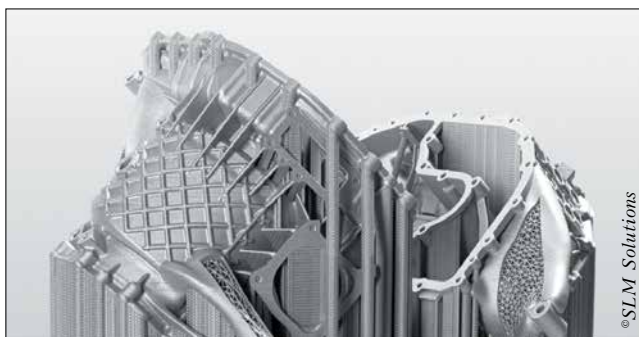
Одно из первых изделий, созданных с помощью 3D-принтера SLM NXG XII 600: металлический корпус силового агрегата E-Drive для спорткара Porsche
